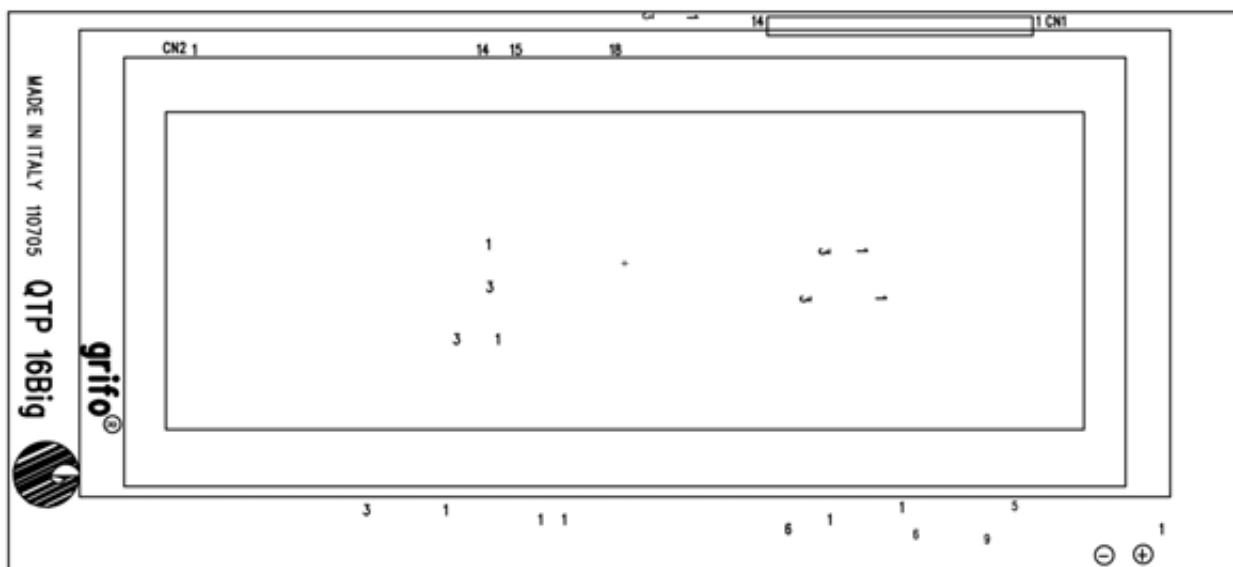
PIANTA COMPONENTI LATO STAGNATURE
